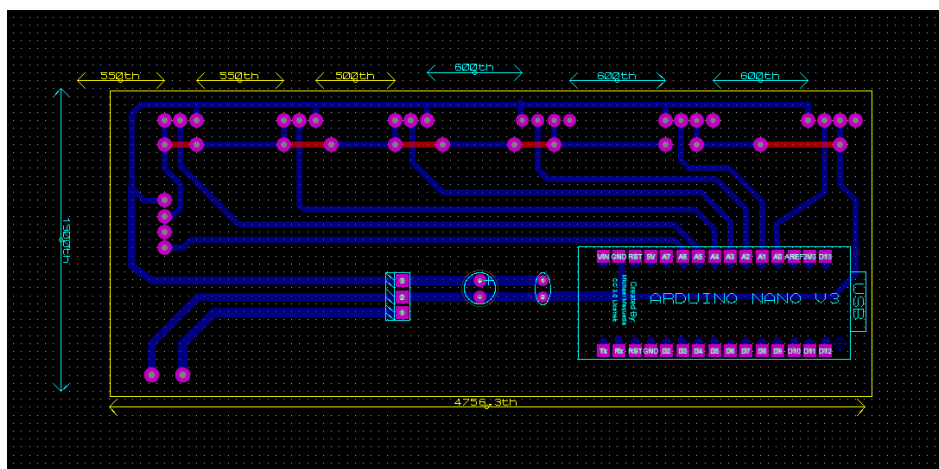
Imagen del diseño de la PCB donde se aprecian las pistas de cobre en el software Proteus
